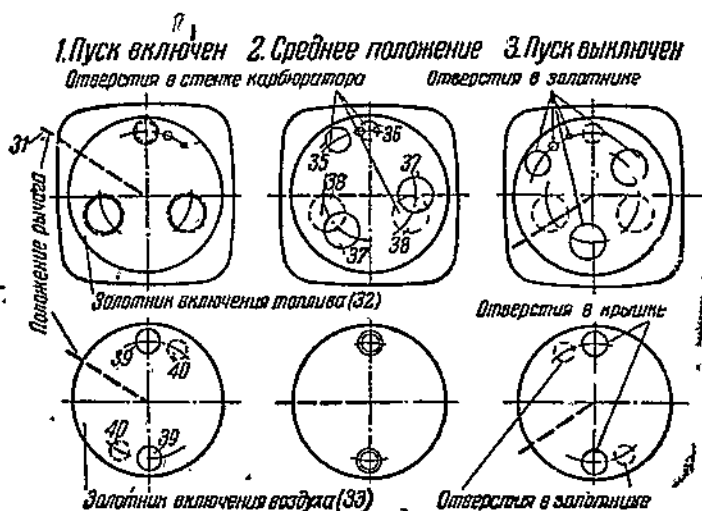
Положения золотников пускового приспособления карбюратора Солекс модели 35-RZFAJPO
